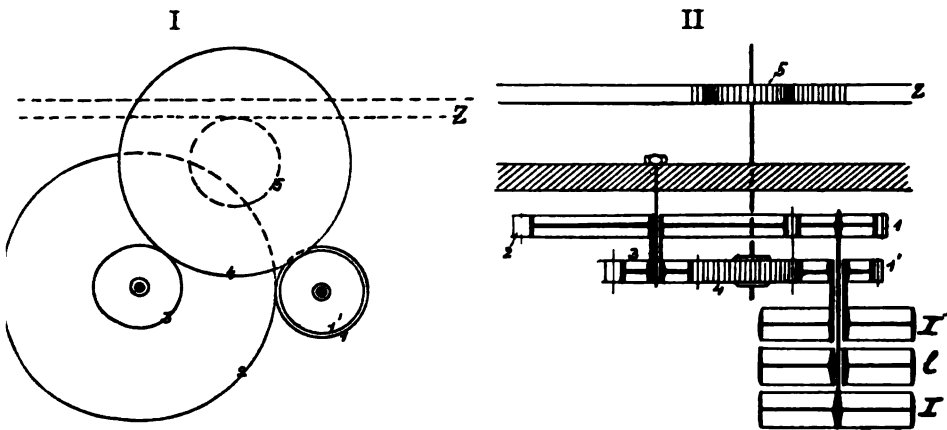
Mechanismus für den schnellen Rückgang bei Hobelmaschinen mit beweglichem Tische.
